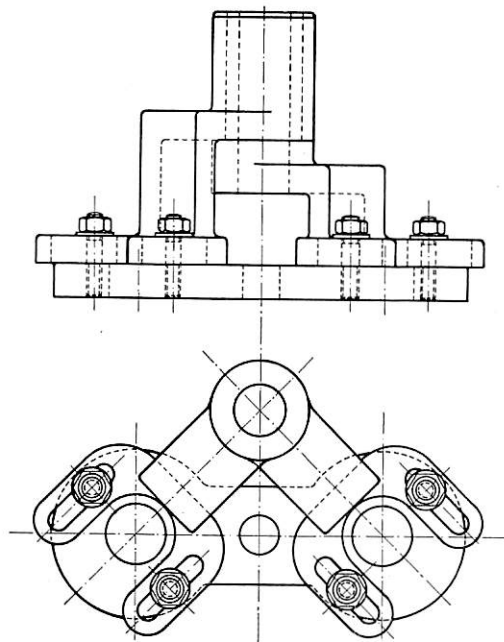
Aufspann-Vorrichtung für Rauchrohrloch-Ausbohr- und Gewindeschneidmaschine.
